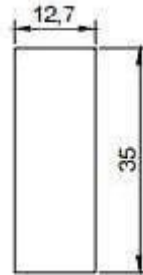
Pieza de guiador a calcular. Vista Izquierda
